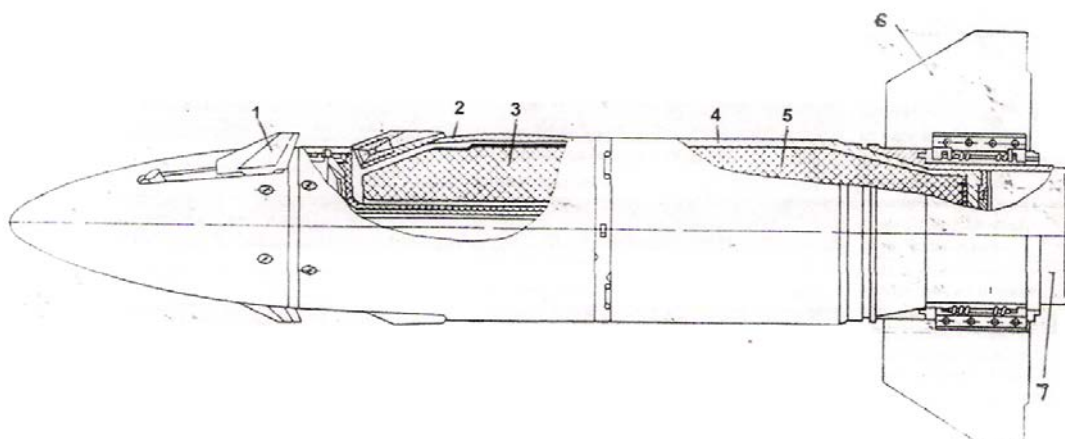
Конструктивная схема ракеты 9М119: 1 – руль; 2 – корпус; 3 – заряд маршевый; 4 – корпус; 5 –кумулятивный заряд; 6 – крылья; 7 – аппаратура приема лазерного излучения
